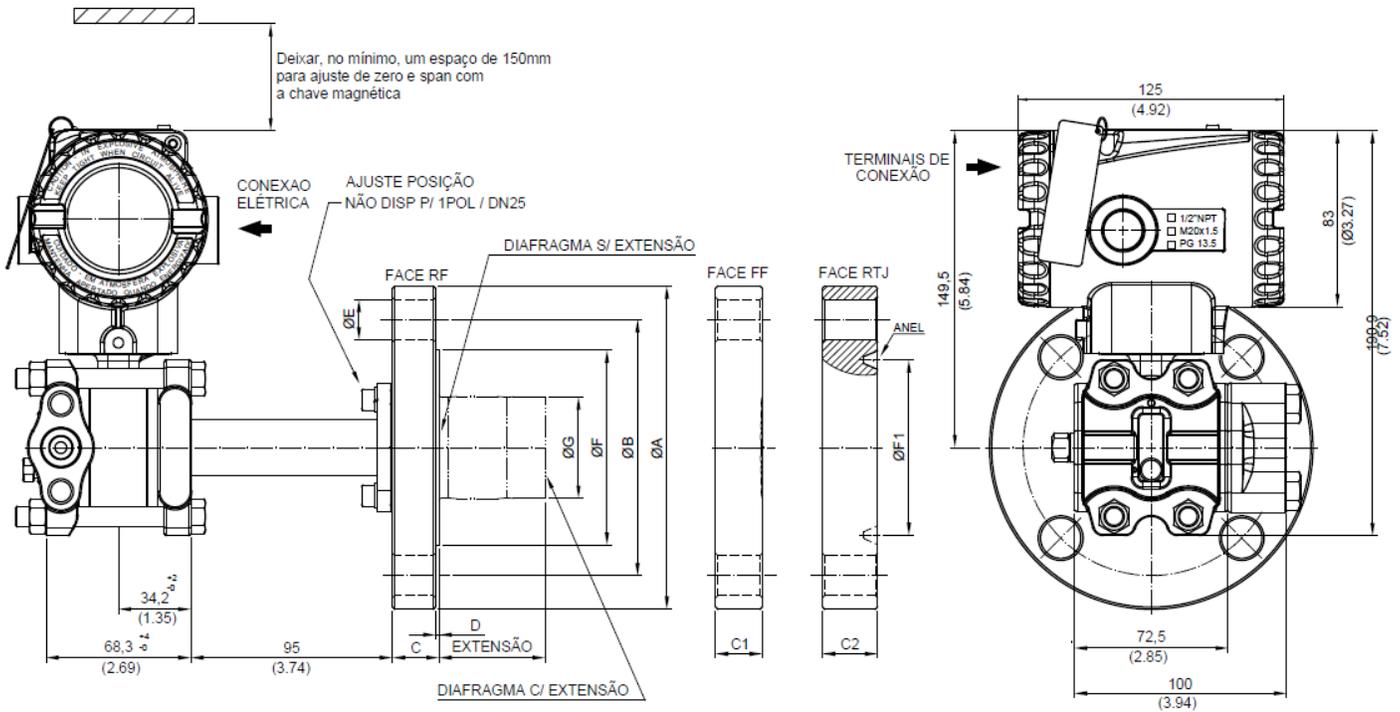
(a) – Desenho Dimensional de Montagem do LD400 HART® - Transmissor de Pressão Diferencial, Manométrica, Absoluta, Alta Pressão Estática e Vazão com Suporte de Fixação
